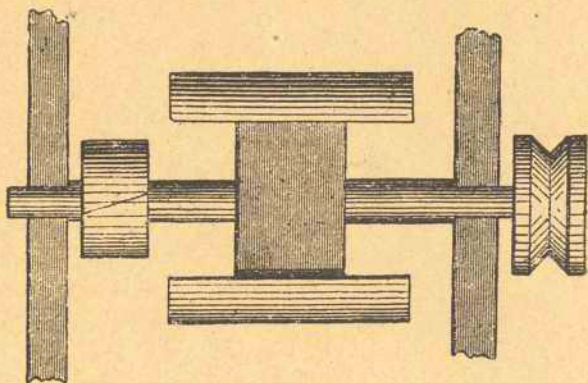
Aspecto exterior de la armadura, conmutador y polea motora.
